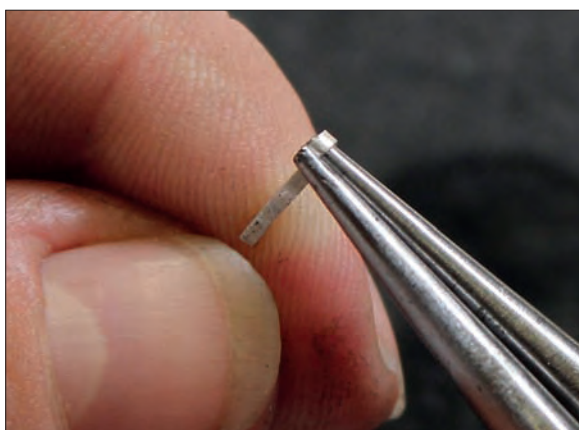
/241: Zastřížení přebytečného materiálu kolem profilované poloviny segmentu. Foto J. Sobek.
